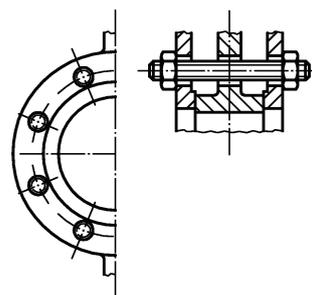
Einklemmklappe mit Monoflansch und Durchgangsbohrungen
